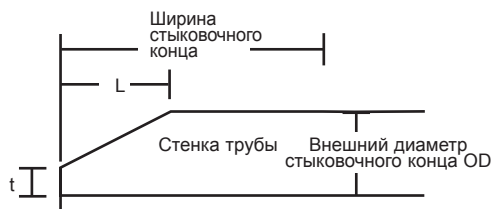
Определения размеров соединительного конца и фаски трубы для муфтового соединения
